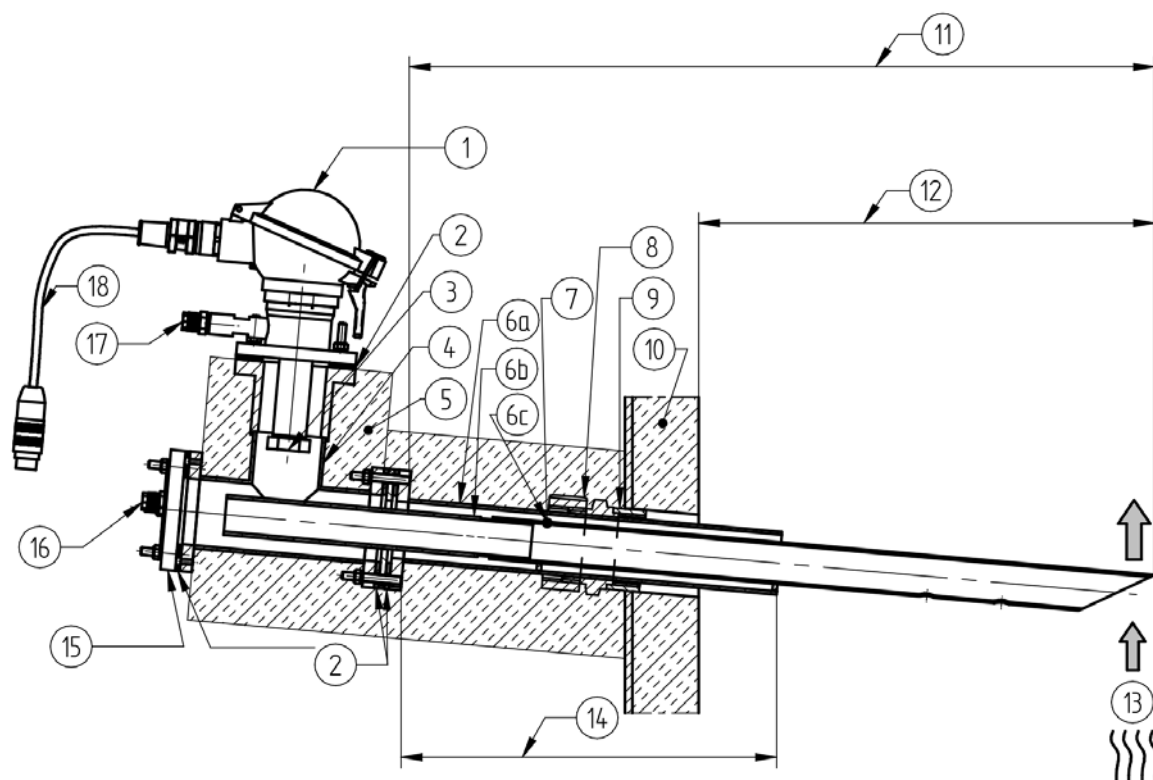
GED FLEX aus Inconel oder Edelstahl mit T-Adapter
